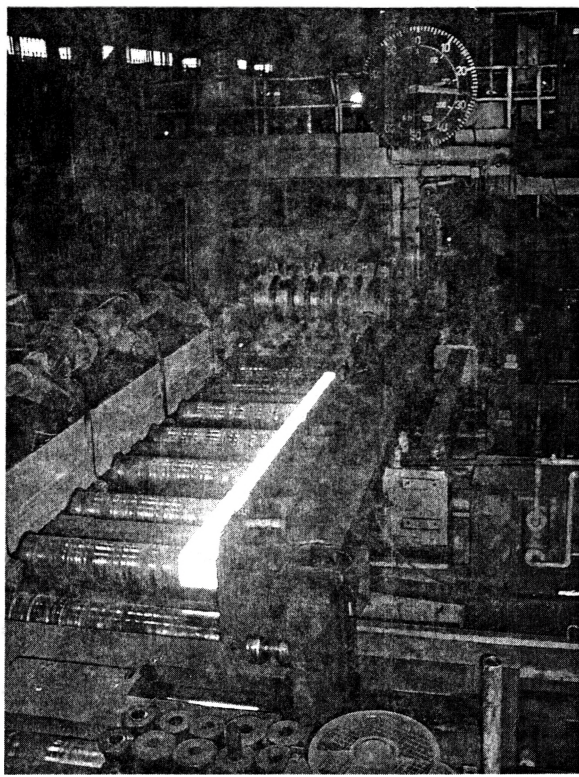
Прокатный стан 850 для производства круглых заготовок диаметром 80... 150 мм и квадратных заготовок сечением 125×125 мм
